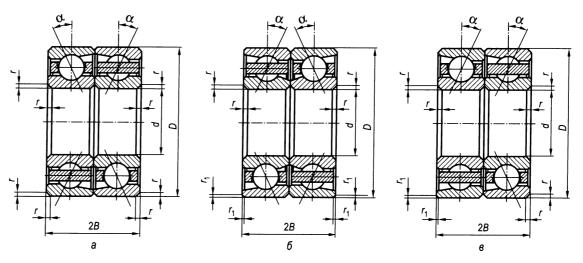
Схемы установки сдвоенных подшипников: a – схема X; δ – схема O; e – схема T
